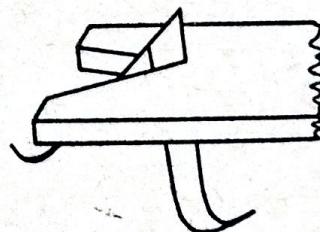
Проверка угла боковой заточки зуба шаблонами
